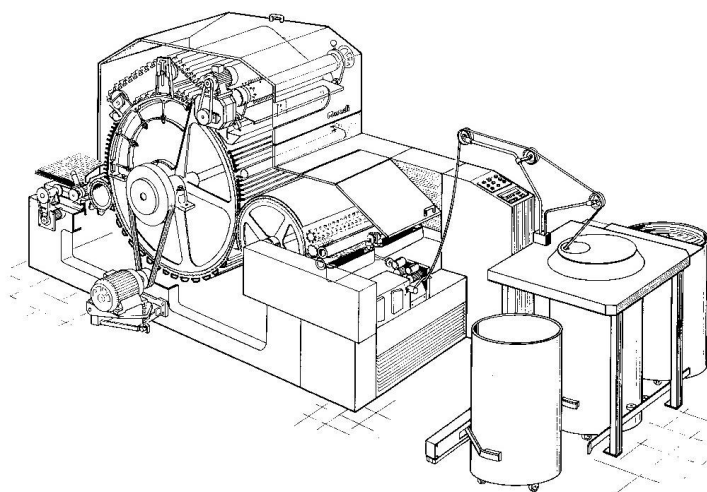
Carda cu lineale (vedere de ansamblu)
